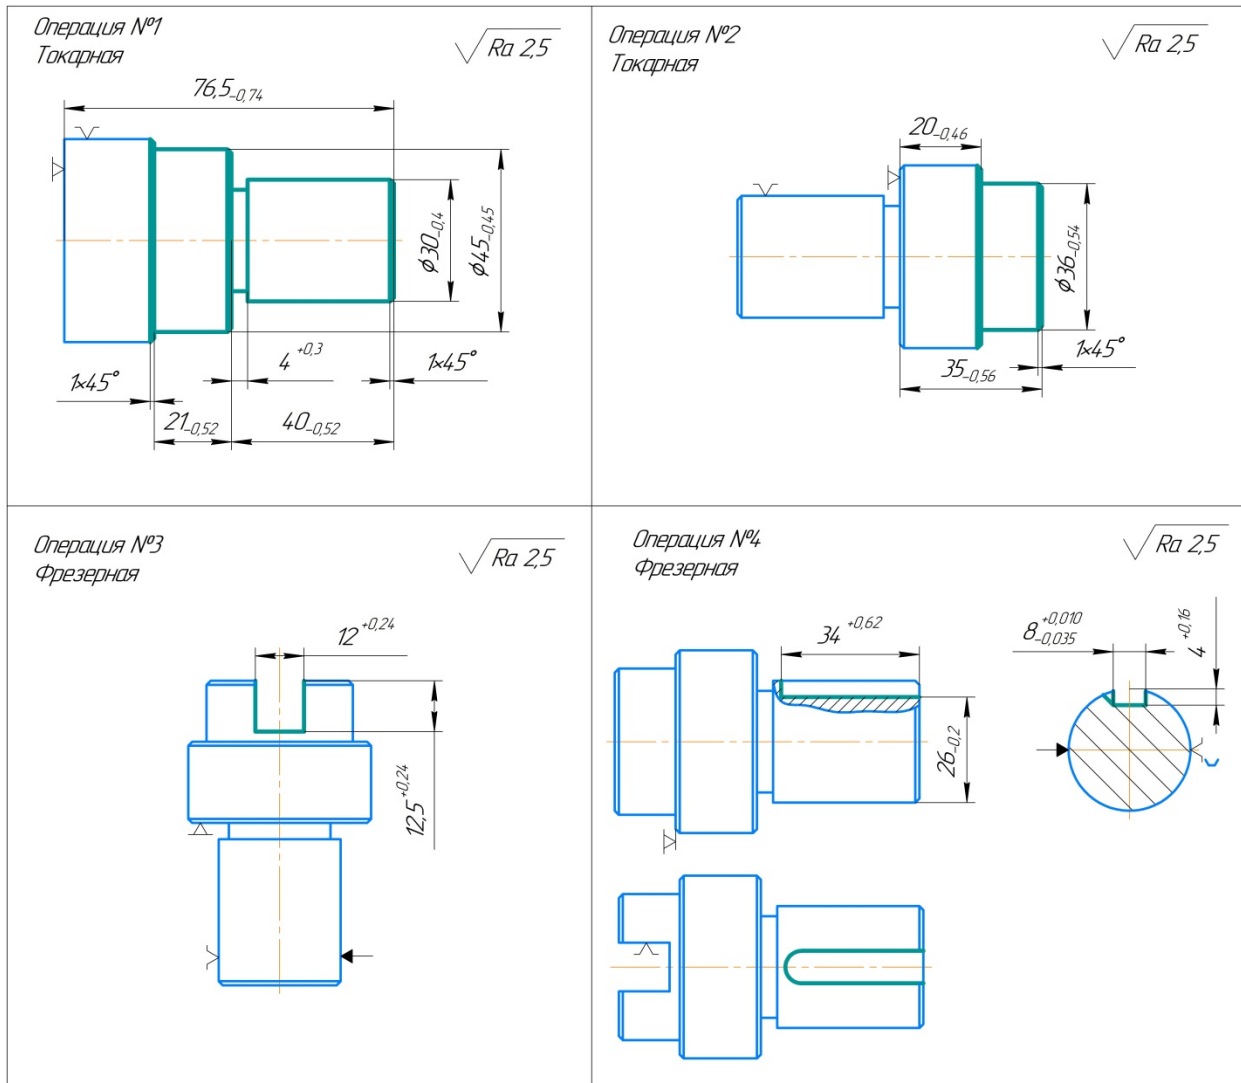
Технологический процесс изготовления детали «Валик»
